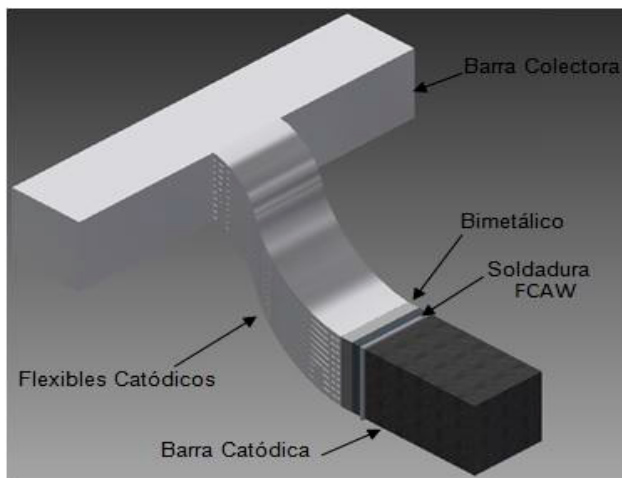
Unión soldada entre barras en celdas P-19
